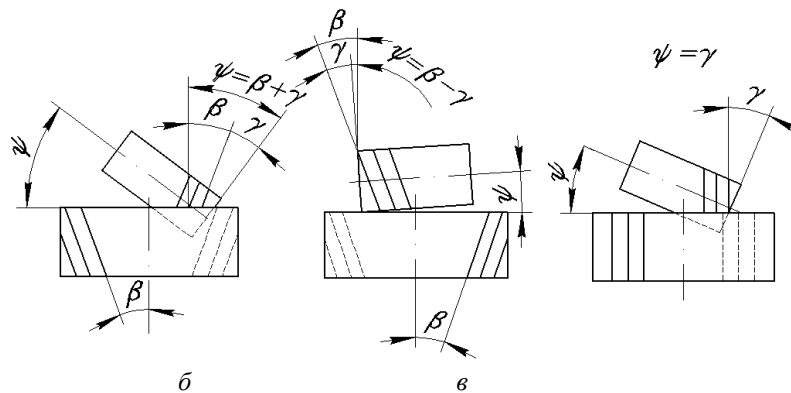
Установка шпинделя фрезы относительно нарезаемых цилиндрических колес: *a* – при разноименных направлениях винтовых линий на фрезе и на колесе; *б* – при одноименных направлениях винтовых линий на фрезе и на колесе; *в* – прямозубых; γ – делительный угол подъема линии витка фрезы; ψ – угол наклона суппорта фрезы
